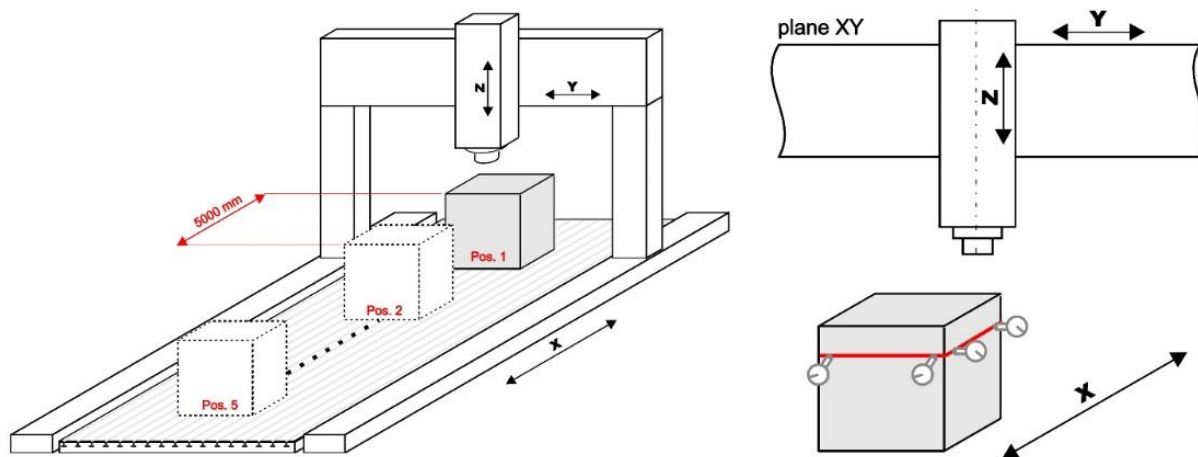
Princip měření kolmosti horizontálních os s jednou pozicí laseru [Renishaw]
